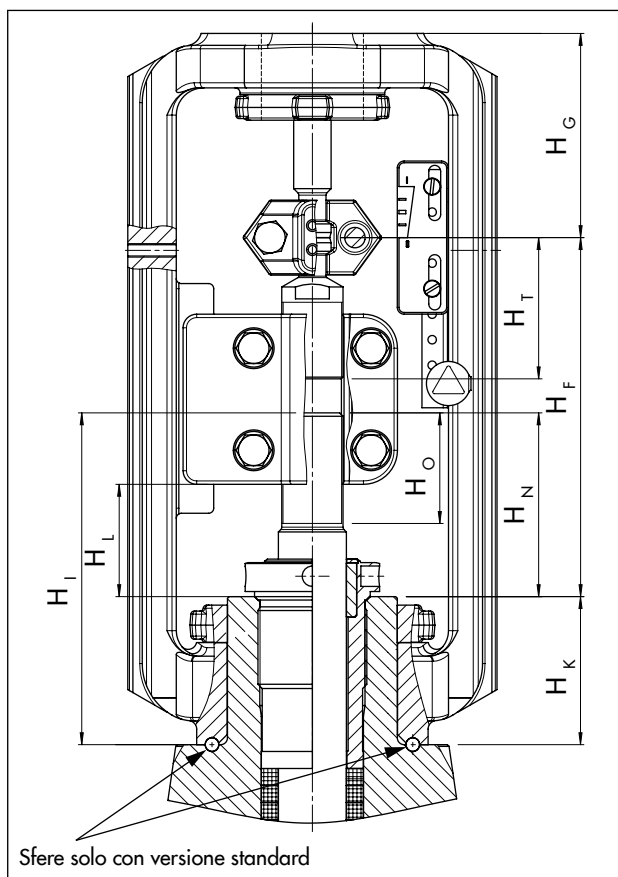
Disegno dimensionale delle dimensioni di montaggio per attuatori pneumatici Tipo 3271 e Tipo 3277
